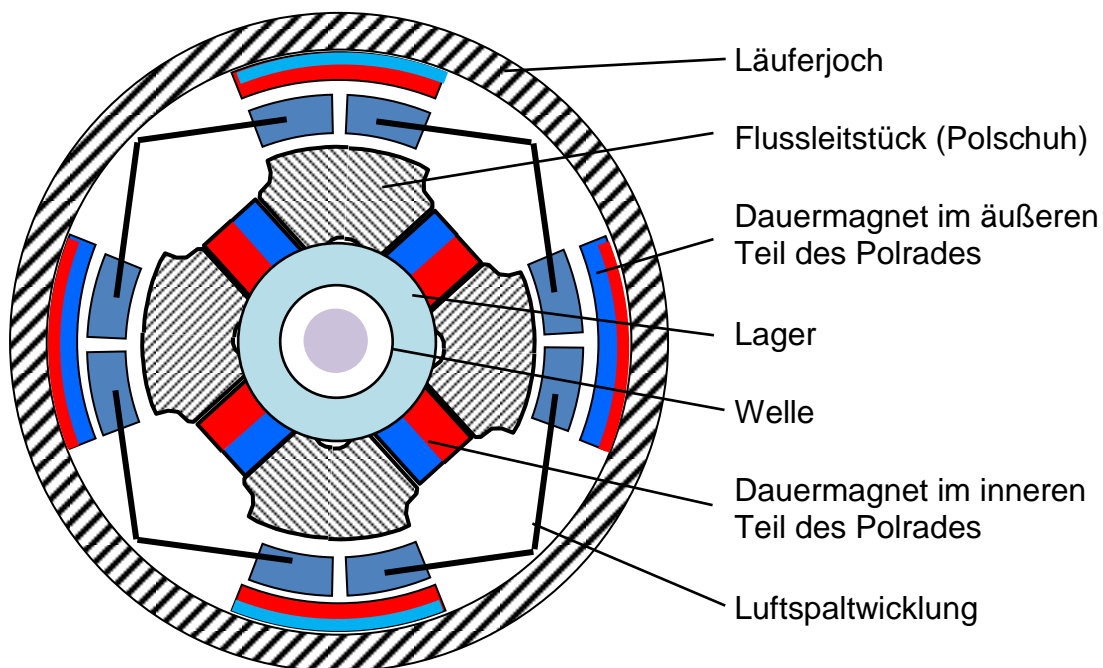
Querschnitt des „Light Spin“ Dynamos ohne Gehäuse
